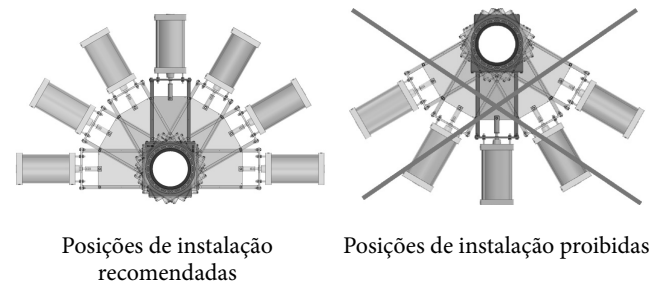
Alternativas de instalação para válvulas SKW e SKF.
